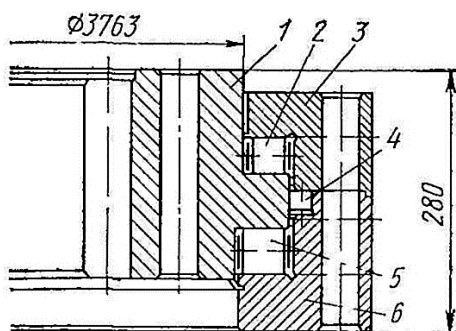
Радіально–упорний підшипник поворотного станду
